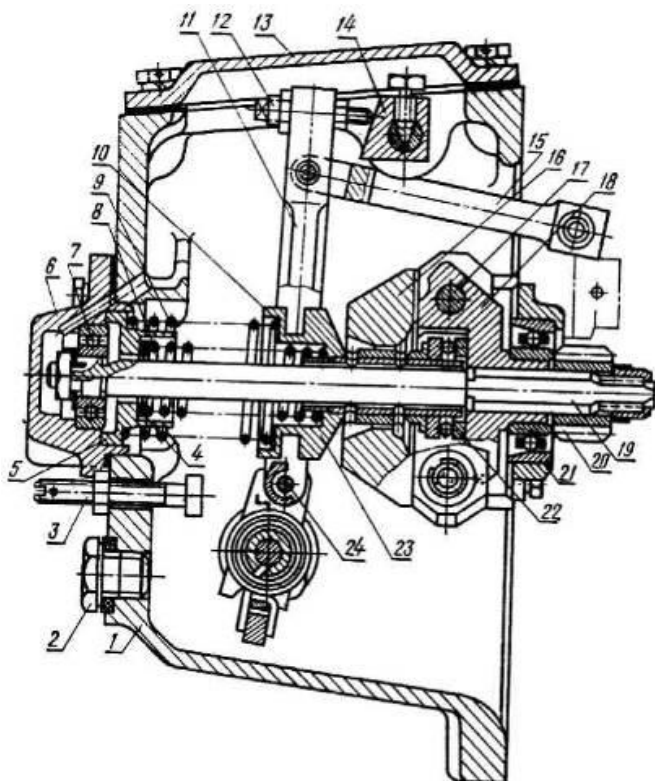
Регулятор насоса 4ТН-9 х 10: 1 - корпус регулятора; 2 - пробка; 3 - болт; 4, 10 - регулировочные прокладки; 5 - седло пружин; 6, 13 - крышки; 7, 21, 22 - подшипники; 8, 9 - пружины; 11 - вилка; 12 - регулировочный винт; 14 - призма корректора; 15 - тяга регулятора; 16 - груз регулятора; 17 - ось груза; 18 - крестовика грузов; 19 - валик регулятора; 20 - шестерня; 23 - муфта регулятора; 24 - ось
